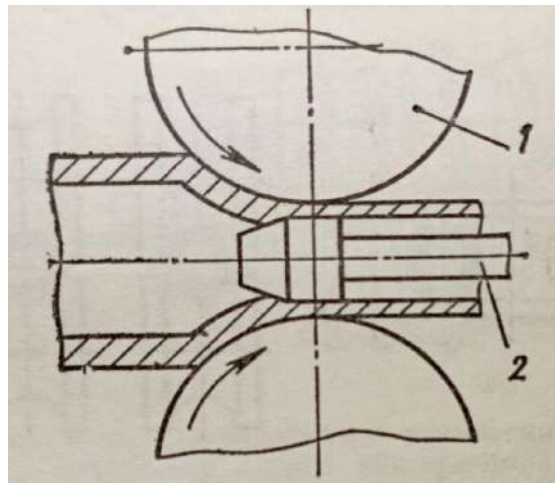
Схема прокатки труб на автоматичному стані:
